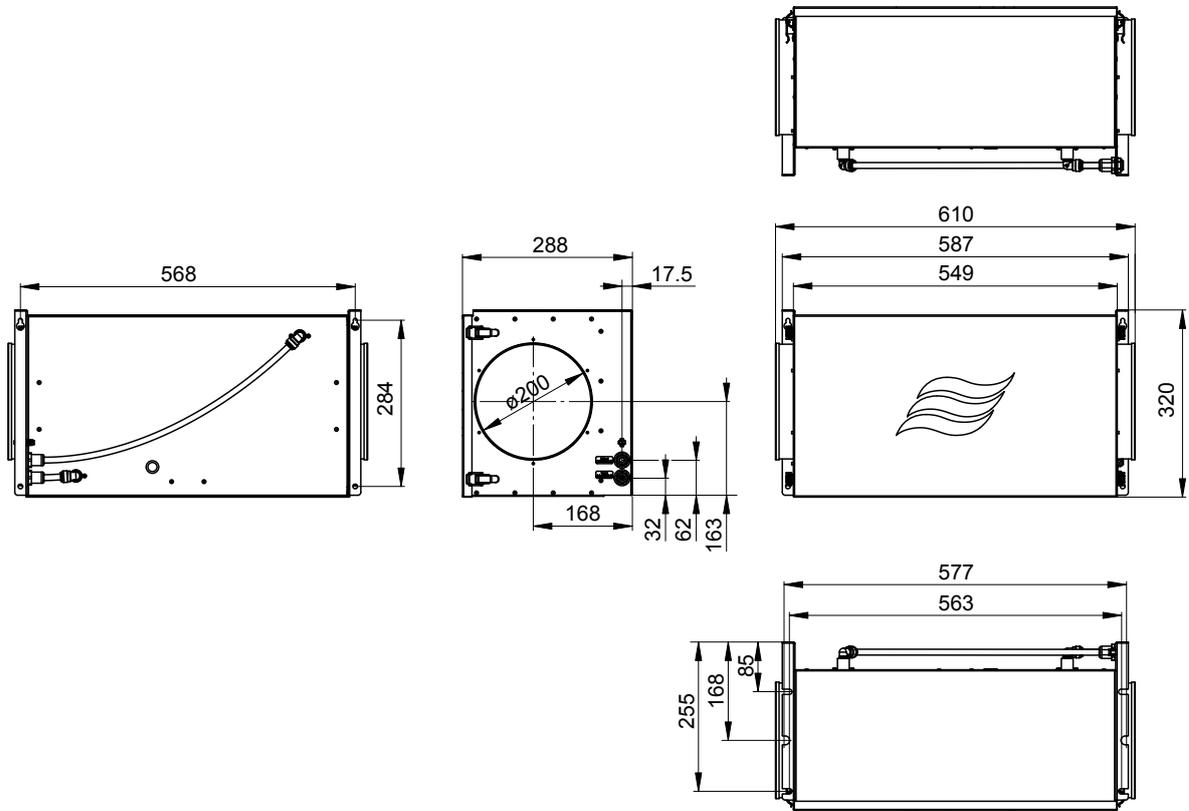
Dimensions unité d'humidification (dimensions en mm)
